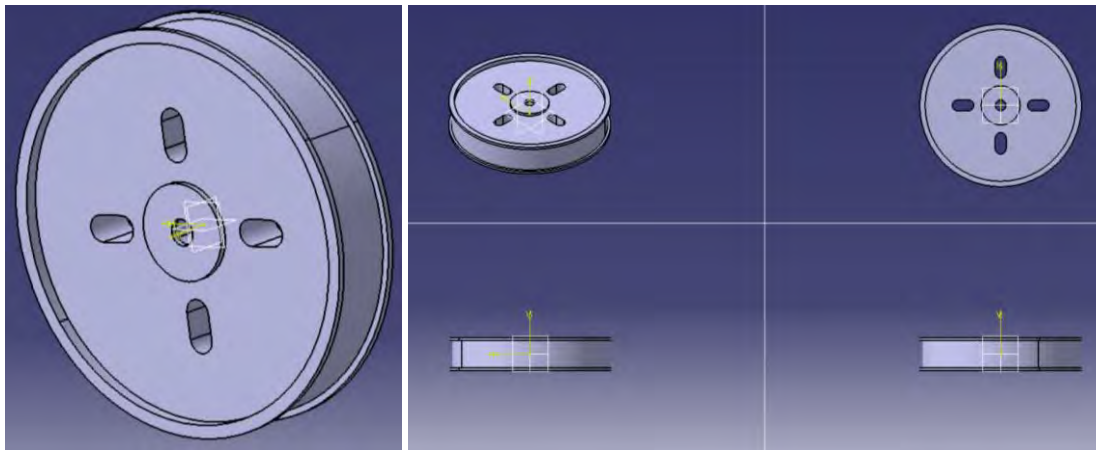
Vistas de dibujo mecánico del rodete compresor estático (realizado en Catia V5)
